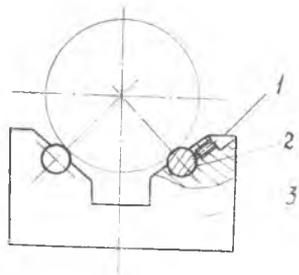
Установка детали на призму с цилиндрическими сухарями
